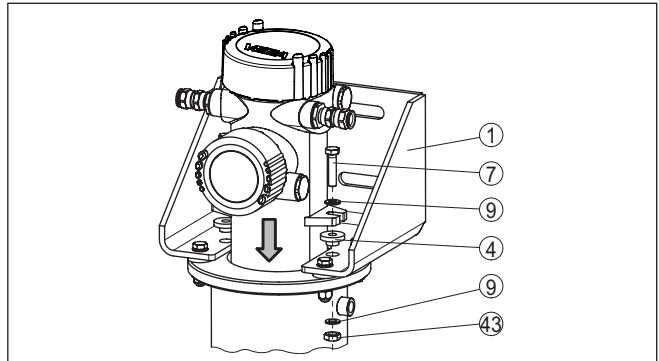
Montage van de sensor - SOLITRAC, POINTRAC
